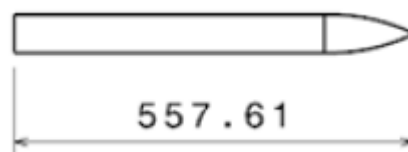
(b) - Dimensões do tubo de cauda + cone de cauda [1]
